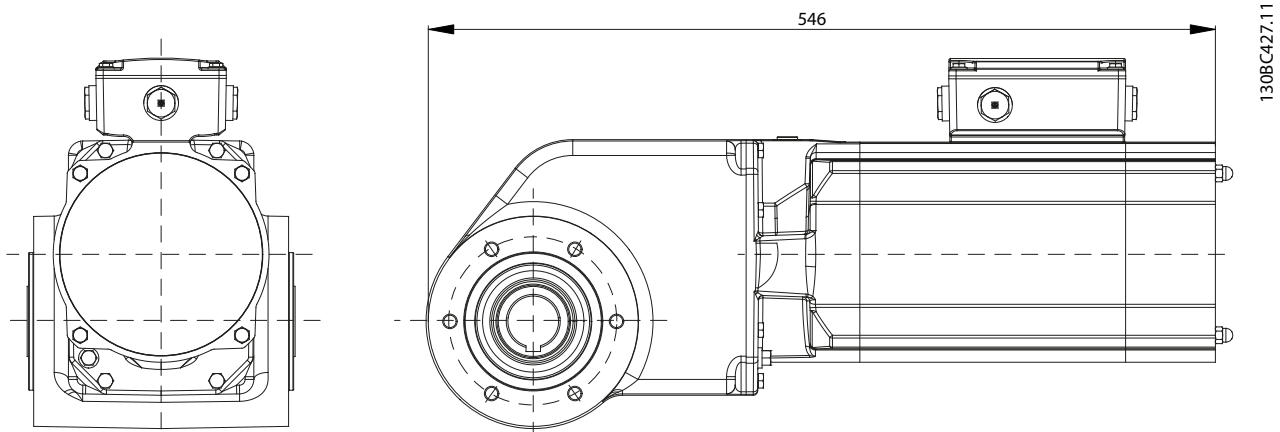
Abmessungen: OneGearDrive mit mechanischer Bremsenoption
